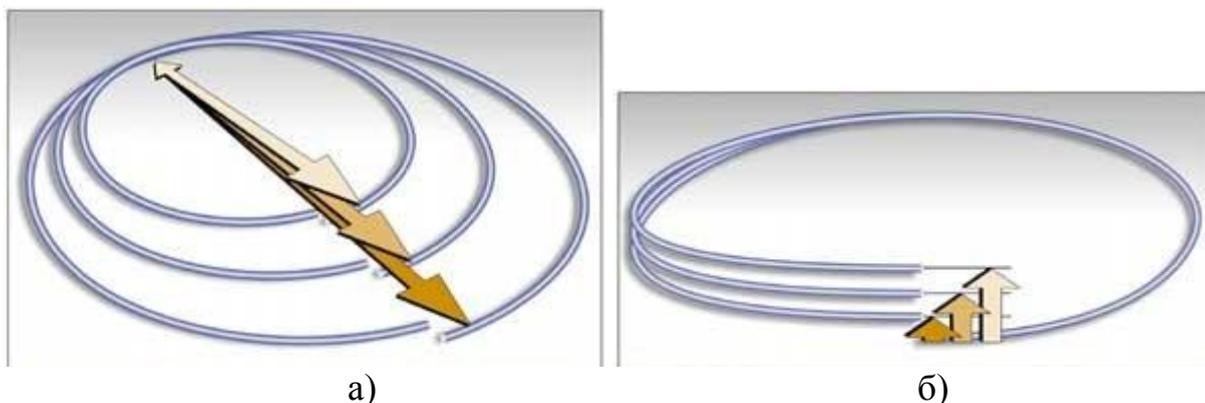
Значения показателей CAST и HELIX сварочной проволоки:
